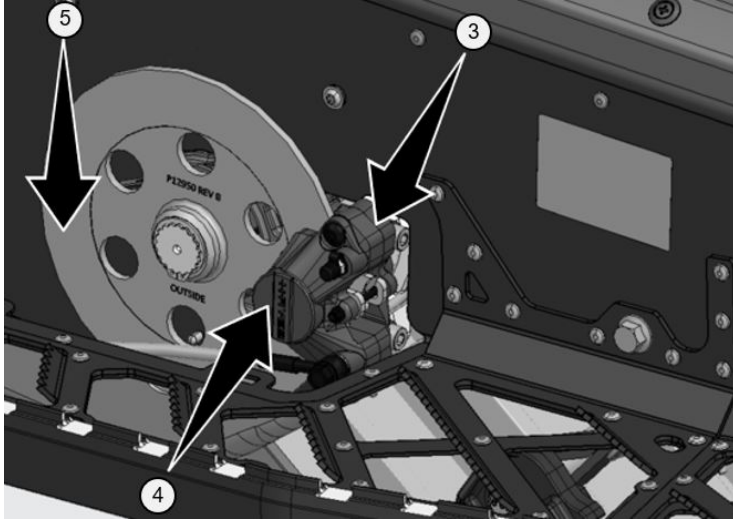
Étrier de frein (3), piston (4) et disque (5) pour inspection
